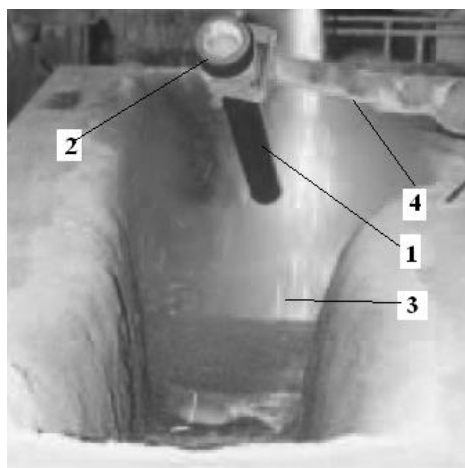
Установка манипулятором защитной трубы сталеразливочного ковша в промежуточном ковше:
